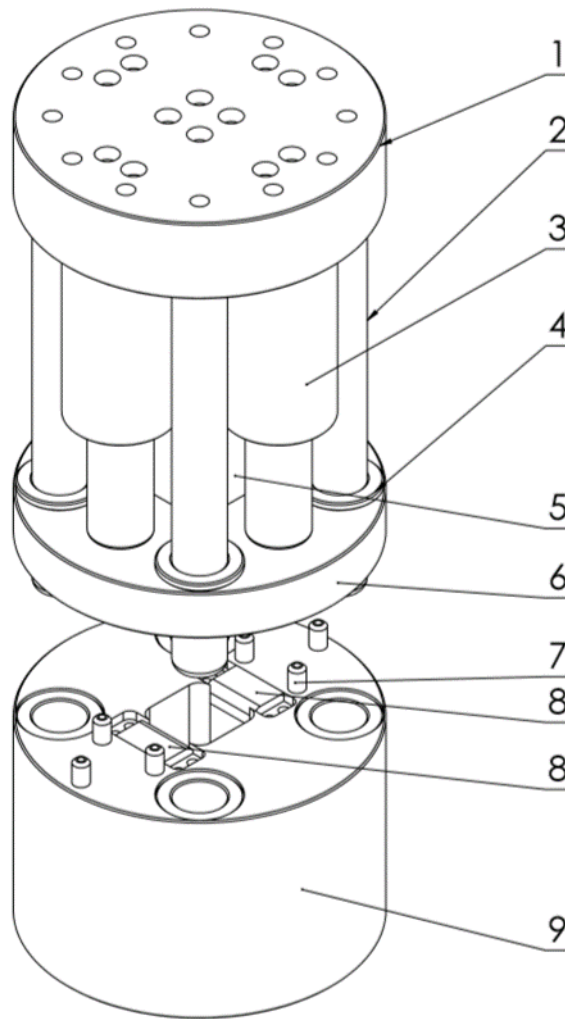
Desenho técnico do dispositivo desenvolvido para estampagem
